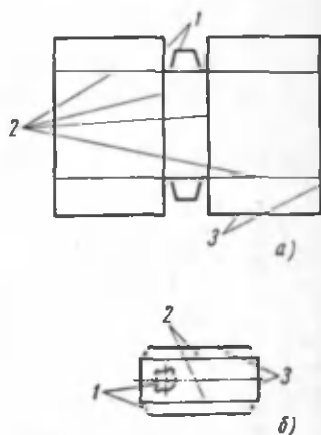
Картонные заготовки корпуса и крышки батареи «Энергия»:
